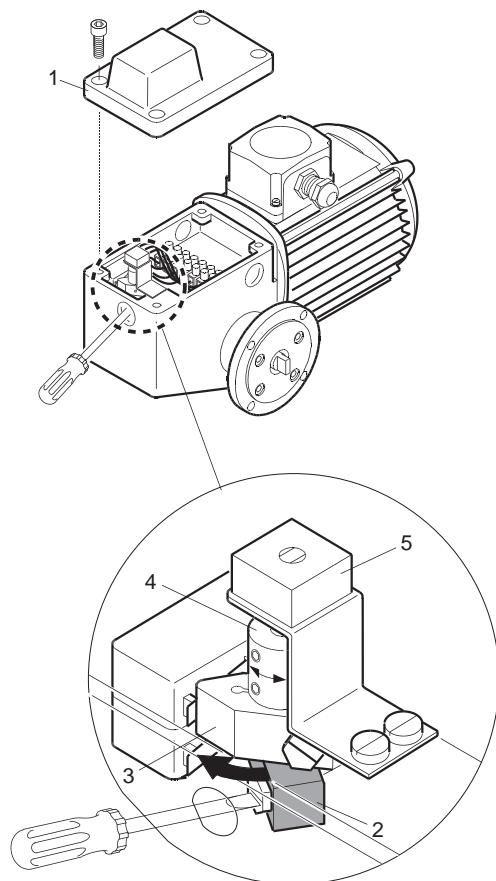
Posizione e vista in dettaglio delle camme di regolazione
